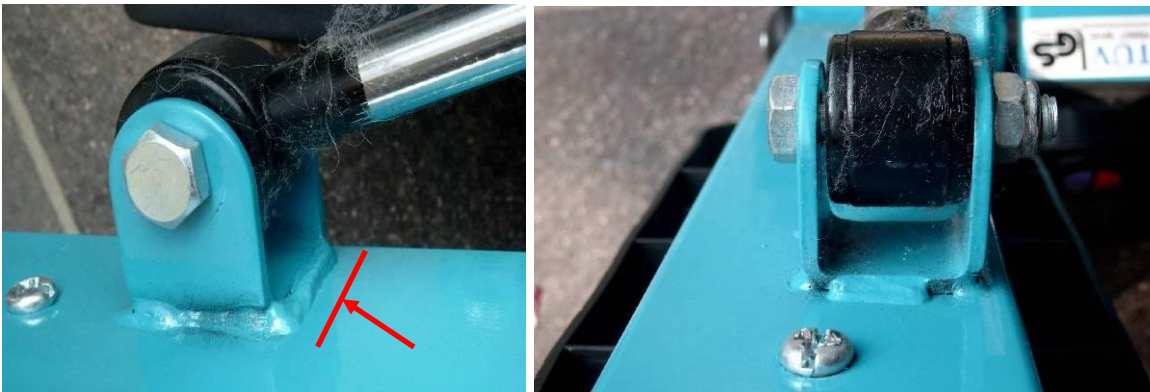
Zugzone mit Schweißnaht Bild 33: außermittige Anordnung
